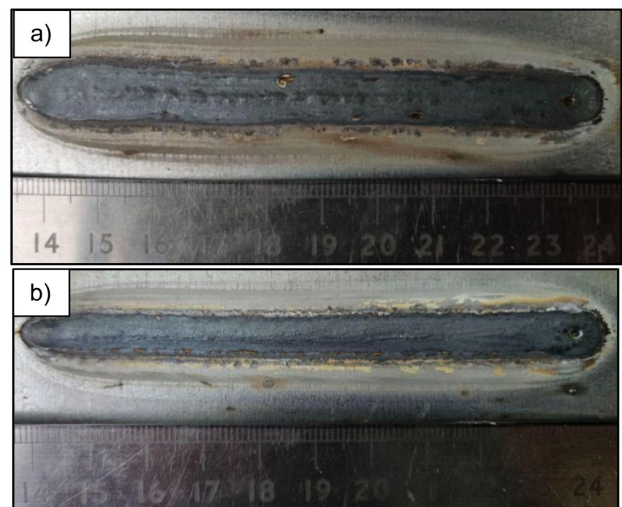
(a) Cordão #11 com maior energia de soldagem e (b) Cordão #13 com menor energia de soldagem.
